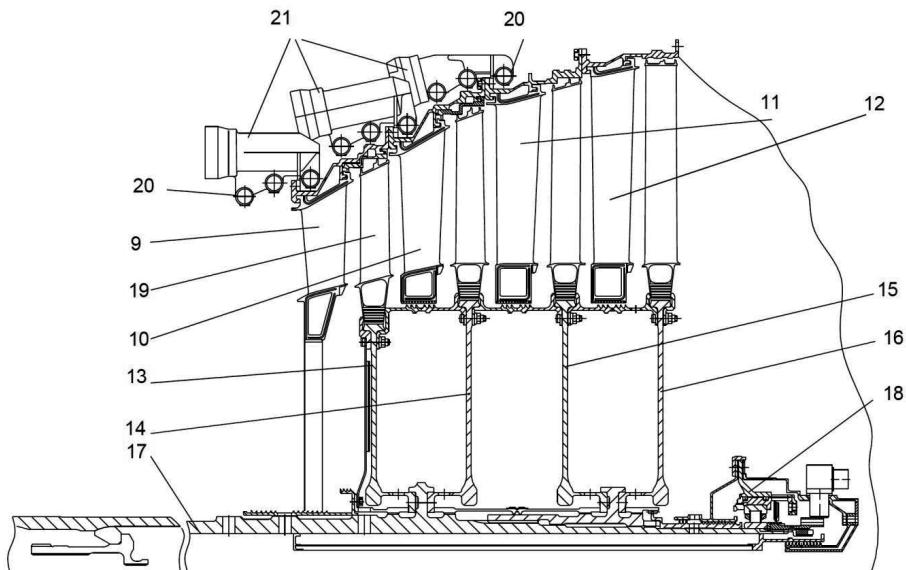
Схема основных узлов турбины низкого давления двигателя ПС-90А:
